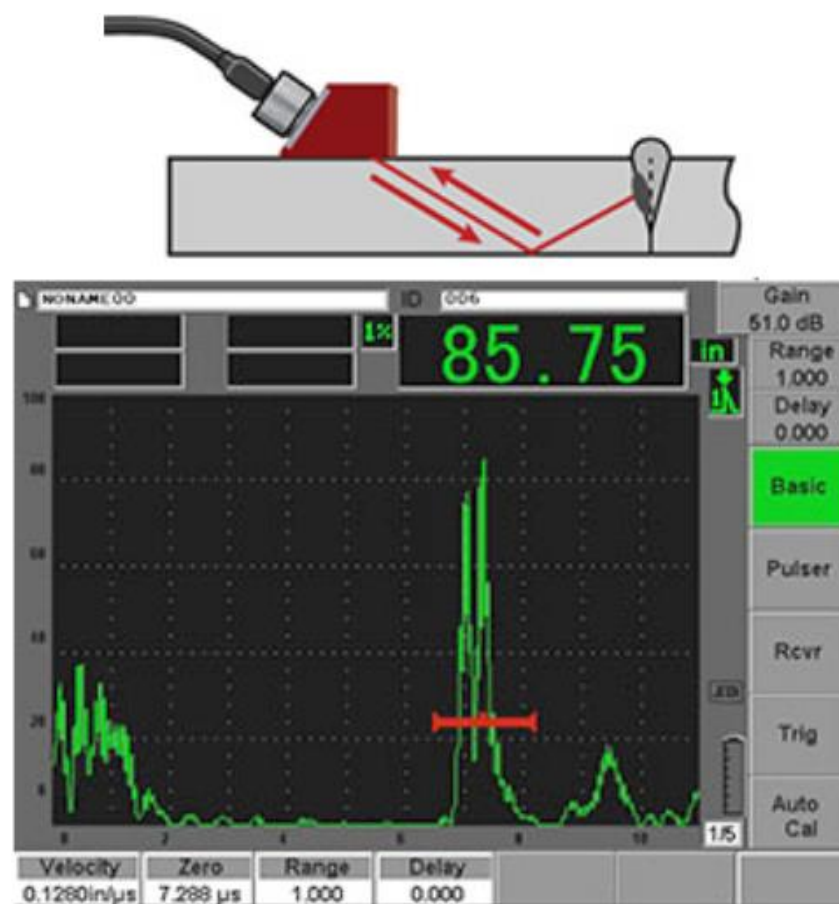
Inspección en UT de cordón de soldadura con defectos
